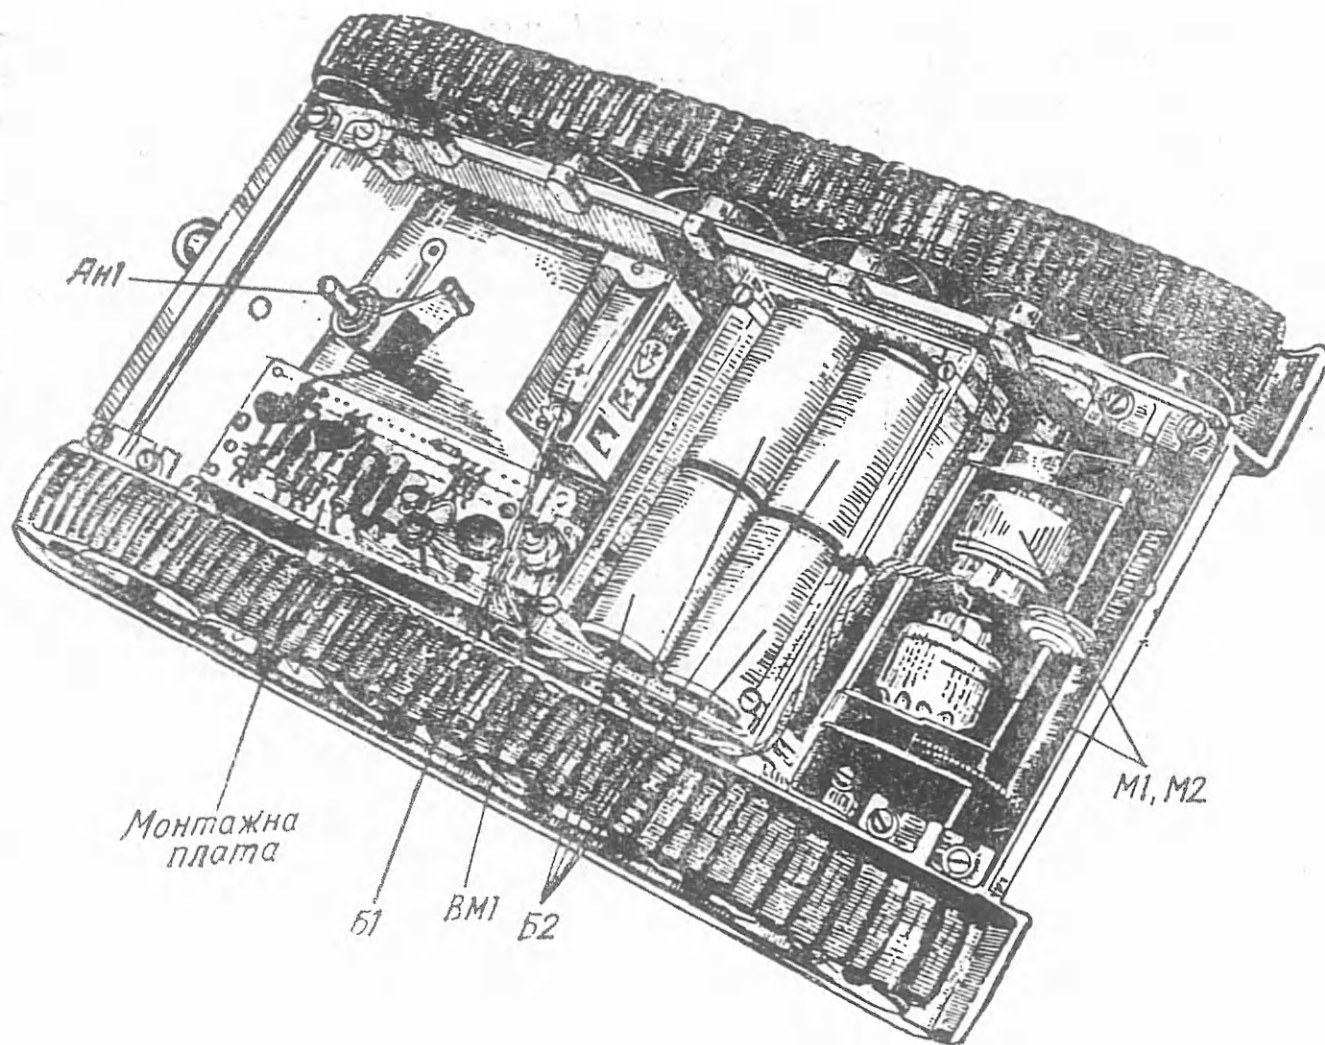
Розташування деталей приймача в корпусі моделі танка.
